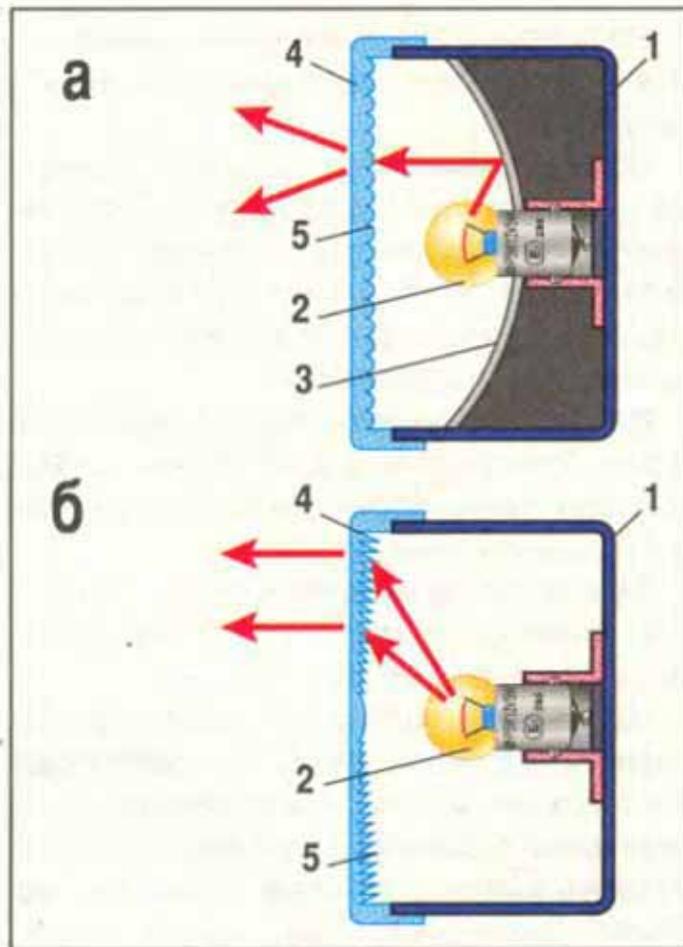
Конструкции фонарей: а – фонарь с отражателем; б – фонарь без отражателя; 1 – корпус; 2 – лампа; 3 – отражатель; 4 – рассеиватель; 5 – линзы.
